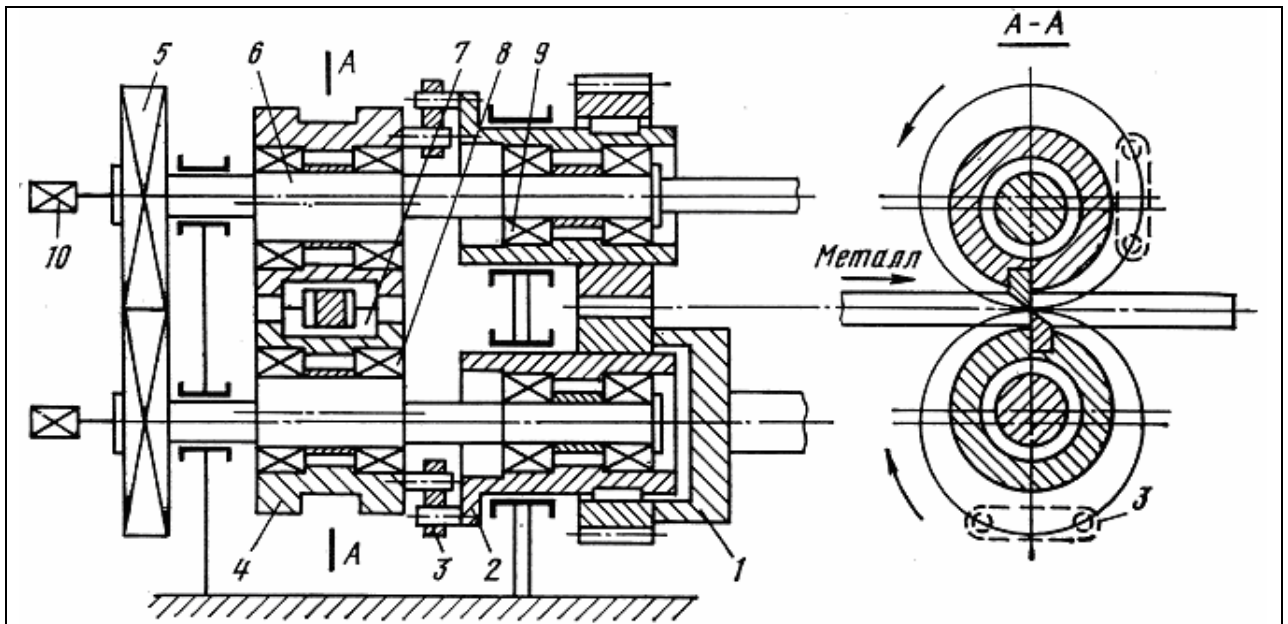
Барабанные летучие ножницы для горячей резки сортовых профилей: 1 – приводные шестерни; 2 – водила; 3 – серьги; 4 – барабаны; 5 – приводимые шестерни; 6 – эксцентриковые валы; 7 – ножи; 8,9 – роликовые подшипники; 10 – сельсины.
